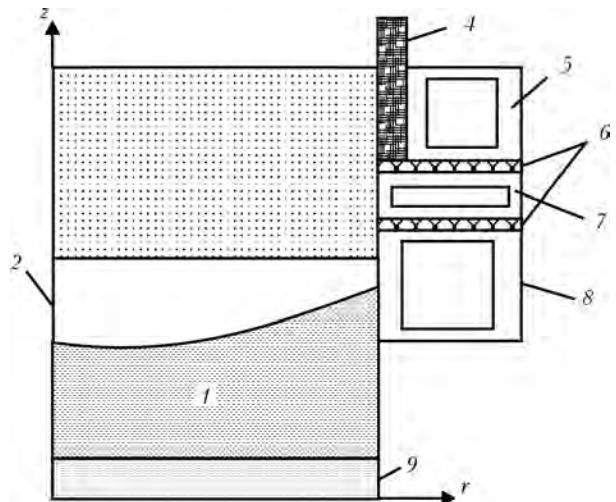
Схема плавки ЭШП в токоведущем кристаллизаторе: 1 – слиток; 2 – металлическая ванна; 3 – шлак; 4 – графитовая футеровка; 5 – токоведущий кристаллизатор под напряжением U ; 6 – изолятор; 7 – кристаллизатор, шунтирующий шлаковую ванну; 8 – кристаллизатор; 9 – поддон
